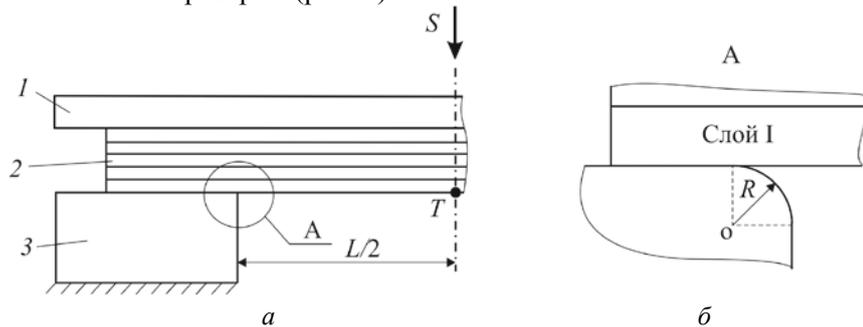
Пакет шпона в прессе: 1 – плита верхней траверсы; 2 – 5-слойный пакет фанеры; 3 – пресс-форма нижней траверсы (S – направление кинематического нагружения)
